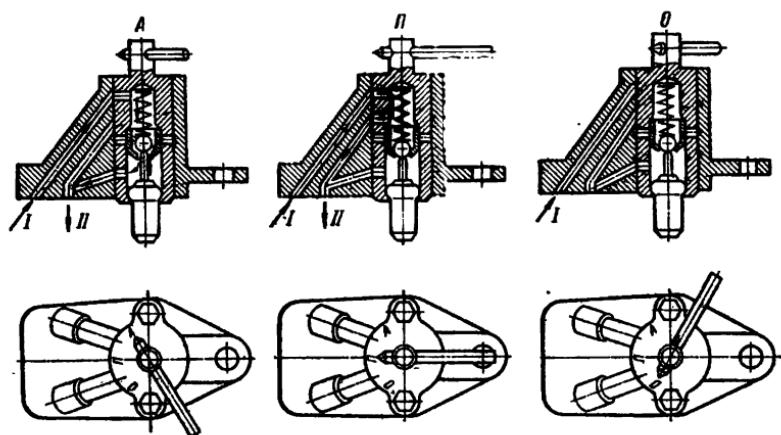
Положения выключателя гидромуфты привода вентилятора:
